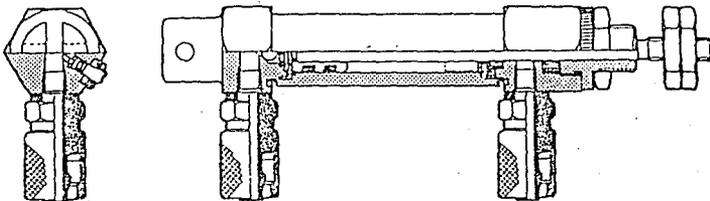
MINI - ACTUADOR DE DOBLE EFECTO.
